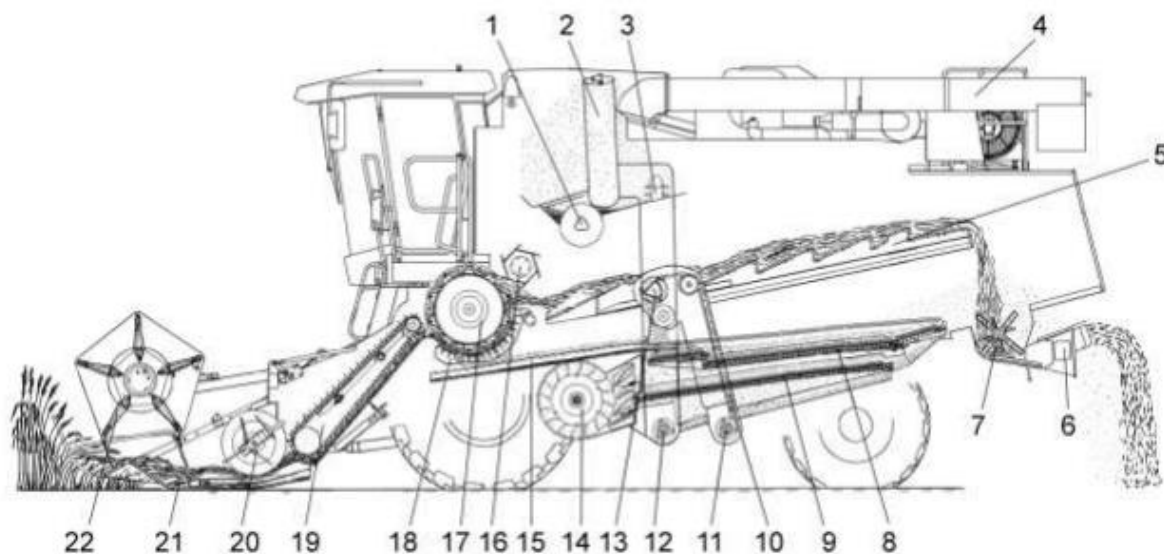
Схема робочого процесу комбайна з класичним МСУ : 1 - шнек горизонтальний; 2 - шнек завантажувальний зерновий; 3 - елеватор зерновий; 4 - шнек вивантажувальний; 5 - соломотряс; 6 - дефлектор; 7 - соломоподрібнювач; 8 - верхній решітний стан; 9 - нижній решітний стан; 10 - елеватор колосовий; 11 - шнек колосовий; 12 - шнек зерновий; 13 - домолочувальний пристрій; 14 - вентилятор; 15 - транспортна (стрясна) дошка; 16 - відбійний бітер; 17 - барабан молотильний; 18 - підбарабання; 19 - плаваючий транспортер; 20 - шнек; 21 - ріжучий апарат; 22 - мотовило
